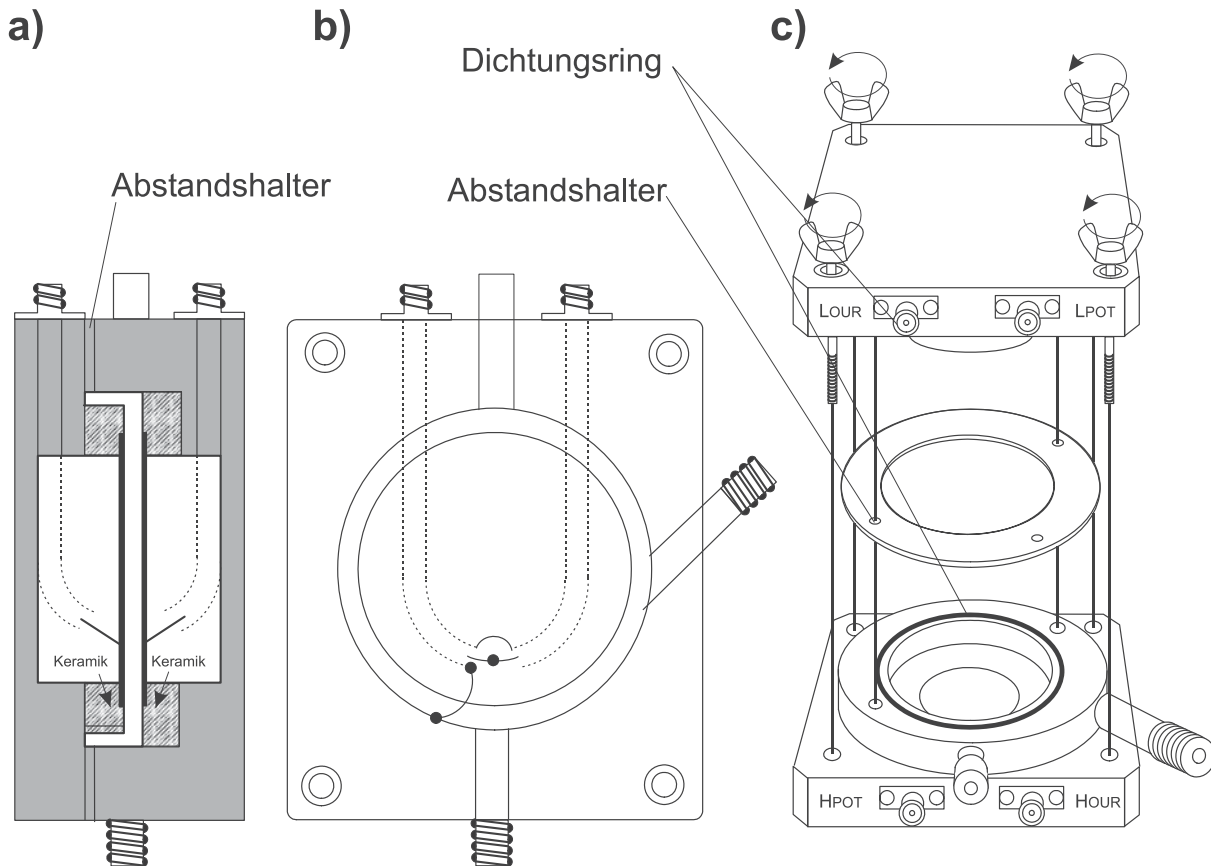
Messzelle; Längs- (a) und Querschnitt (b) sowie Explosionszeichnung (c),
